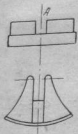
Фрезеровка гнезда для ремонтюара.
